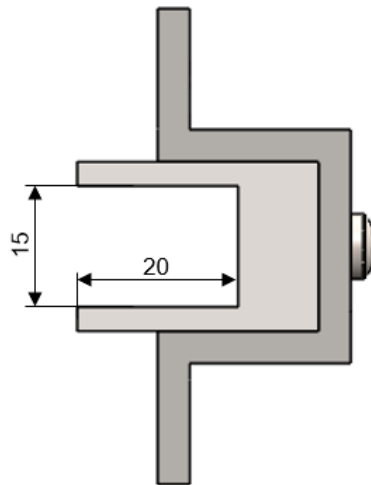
Secção da calha de deslizamento, dimensões em mm
